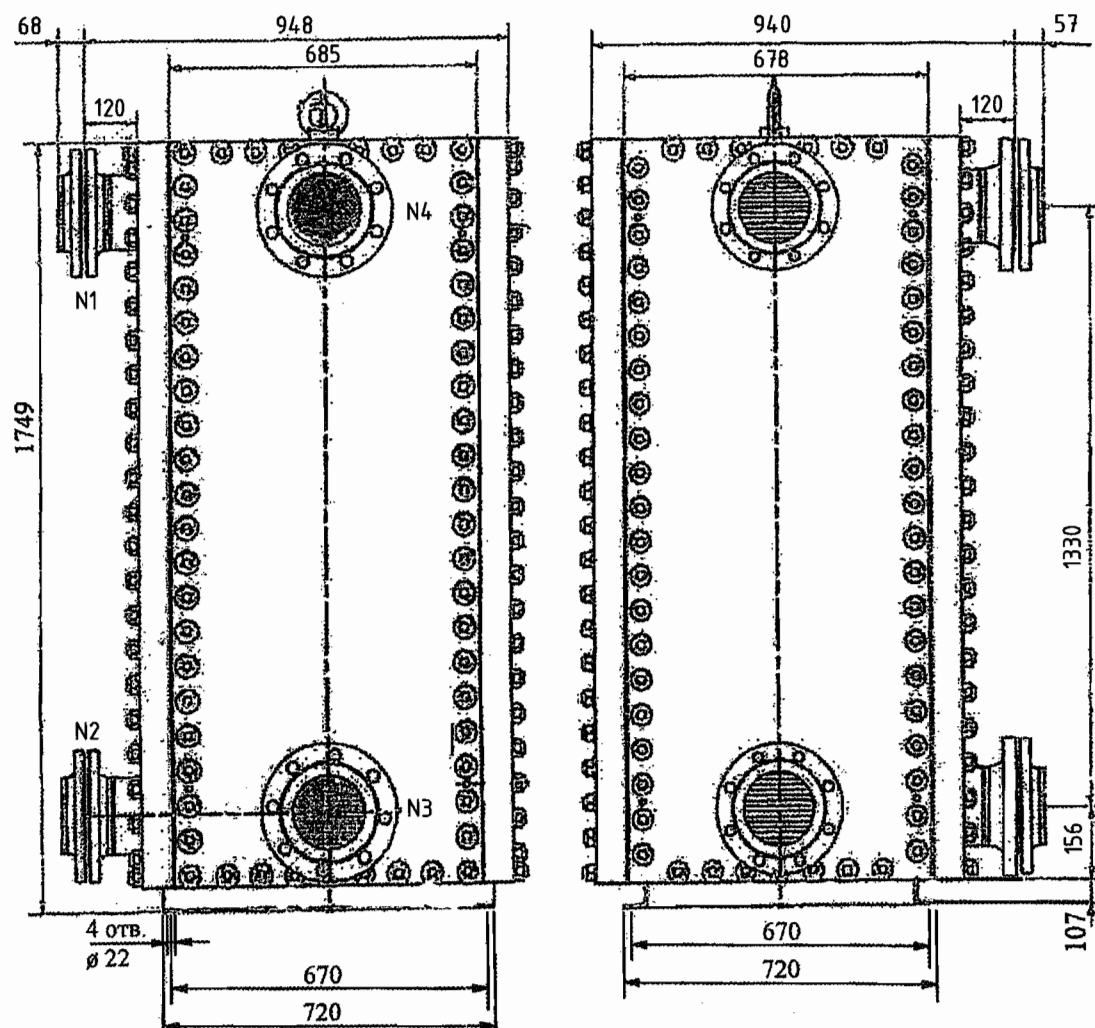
Габаритный чертеж доохладителя продувки парогенераторов
